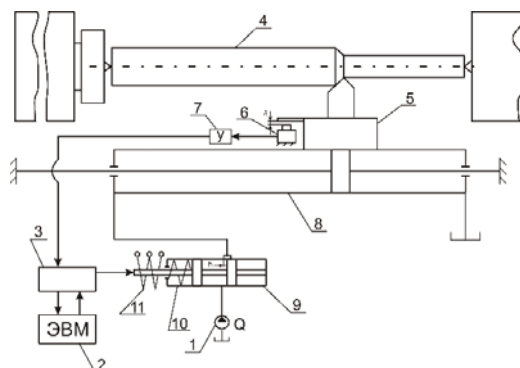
Принципиальная схема однокоординатного гидроконтролируемого устройства для токарного станка: 1 – гидравлический насос; 2 – компьютер; 3 – интерфейс; 4 – обрабатываемая деталь; 5 – суппорт с резцом; 6 – датчик упругих перемещений; 7 – усилитель; 8 – силовой цилиндр; 9 – золотник; 10 – пружина; 11 – электромагнит.
